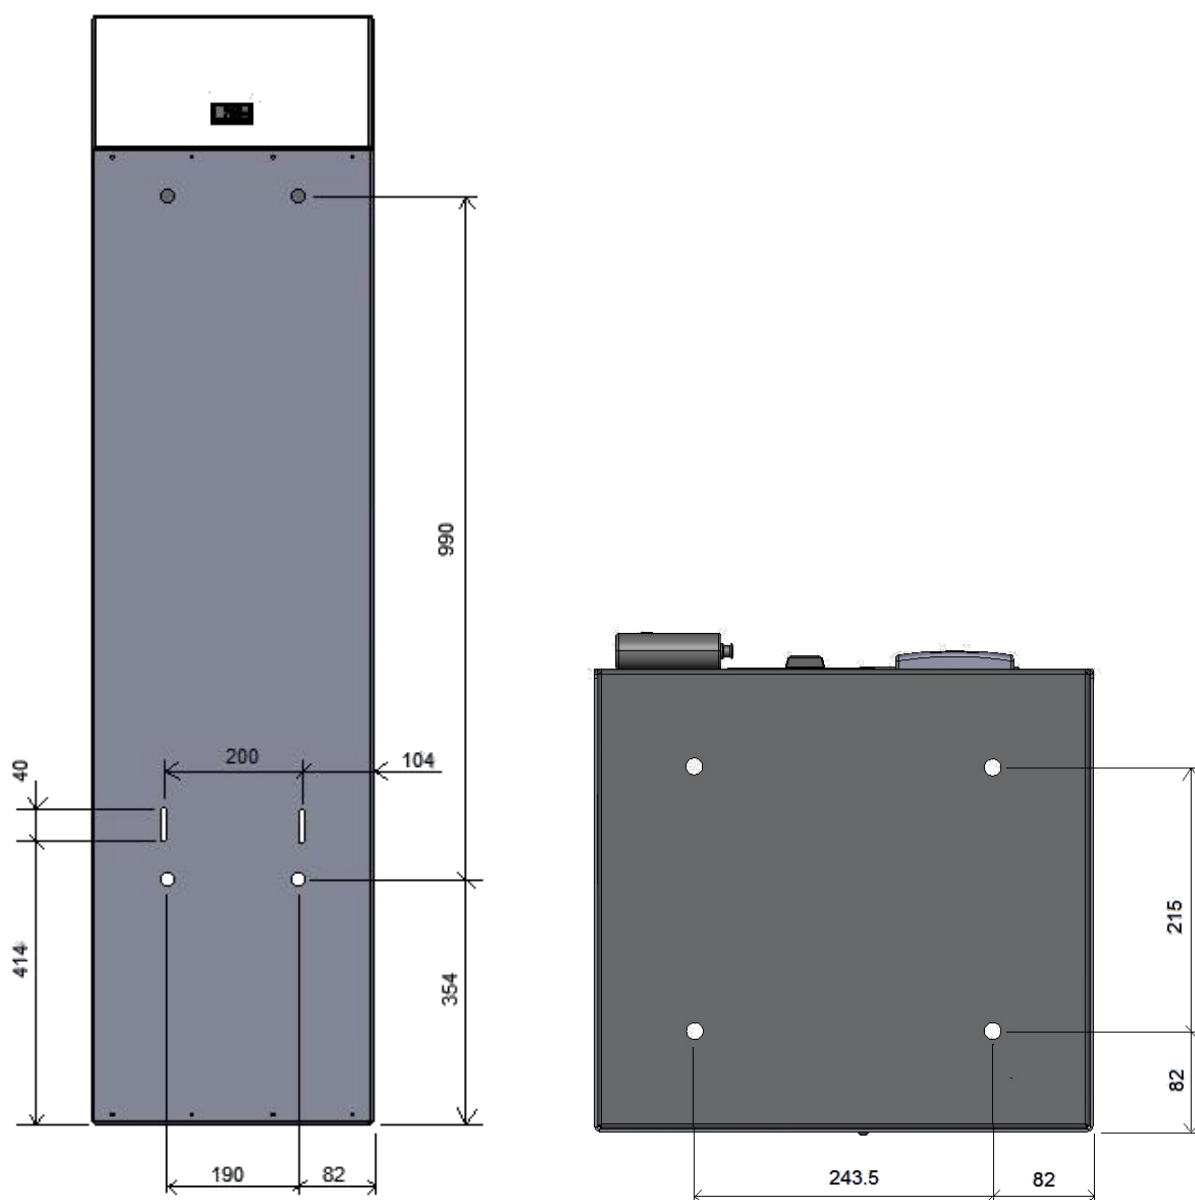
Dima fori di fissaggio a parete (fig. sinistra) e pavimento (fig. destra)
